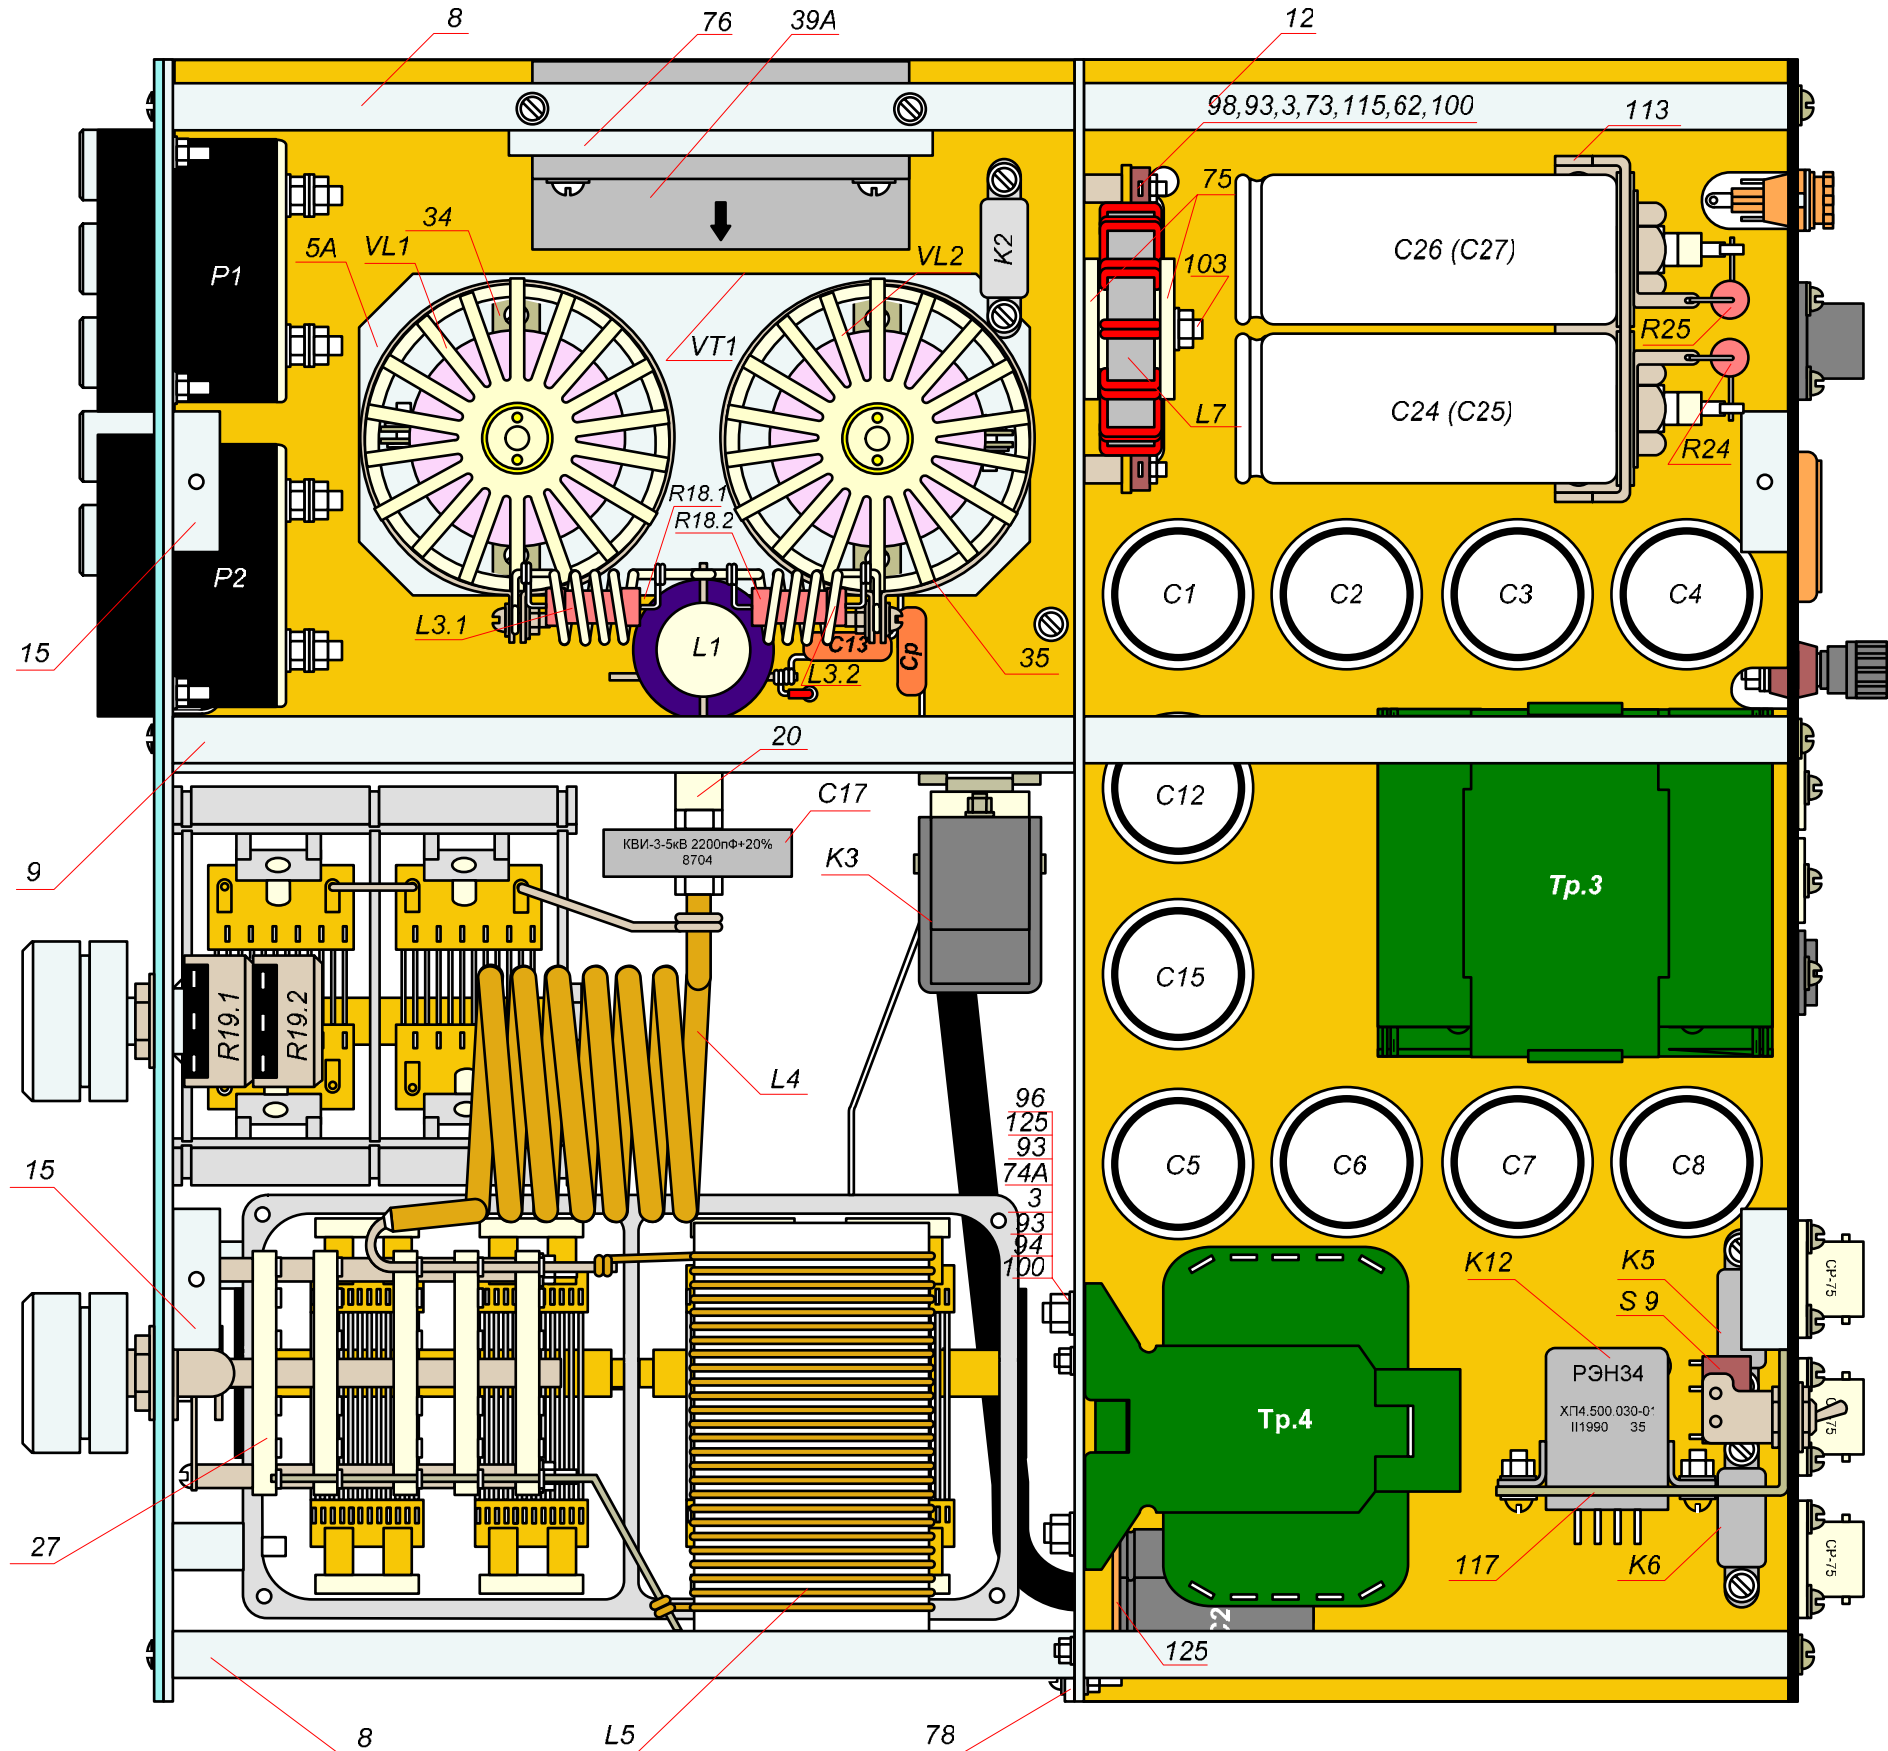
А. Сборочный чертёж усилителя ДУА-300А. Вид снизу со снятой нижней крышкой.
